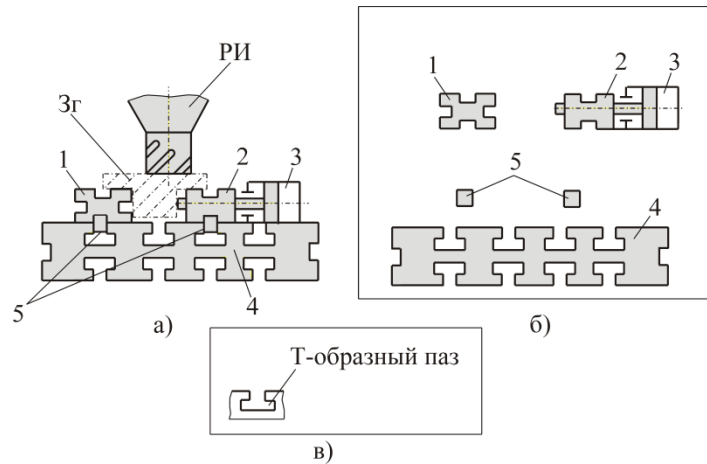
Схема СП тисочного типа системы УСП с механизированным зажимом: 1 – опора левая; 2 – опора правая; 3 – силовой привод; 4 – плита; 5 – шпонки
